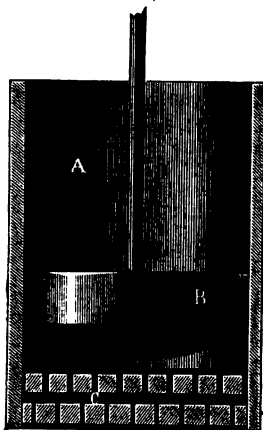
stellt einen solchen Apparat dar. A ist ein gußeiserner Cylinder, welcher mit einem Dampfmantel umgeben ist. Die aufgeweichte Guttaperchamasse wird mittels des Kolbens B durch den durchlöchernten doppelten Boden C des Cylinders A gepreßt, während die darin befindlichen Unreinigkeiten mechanisch zurückgehalten werden.
